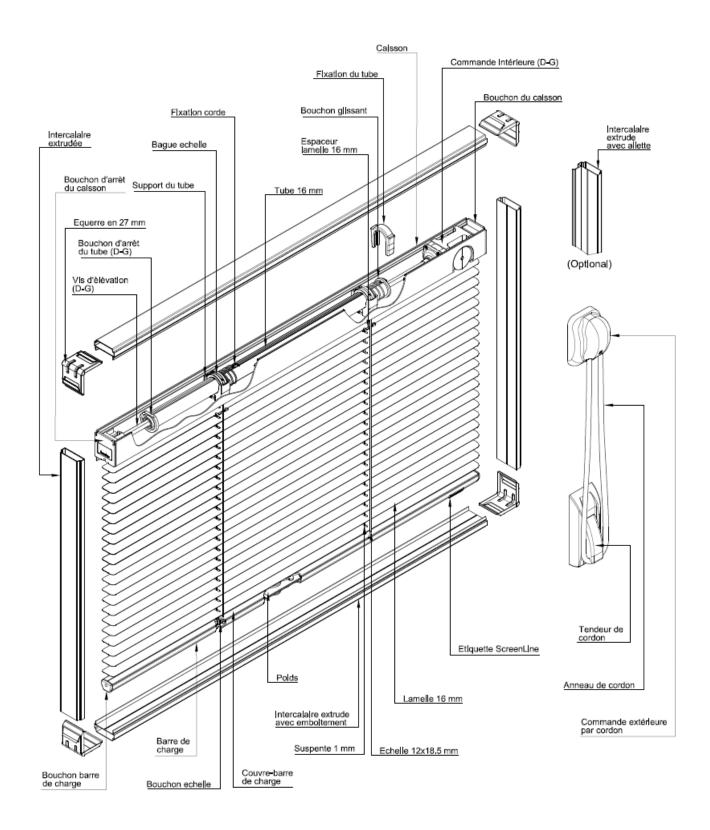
Vue d'ensemble éclatée - Store en position basse
